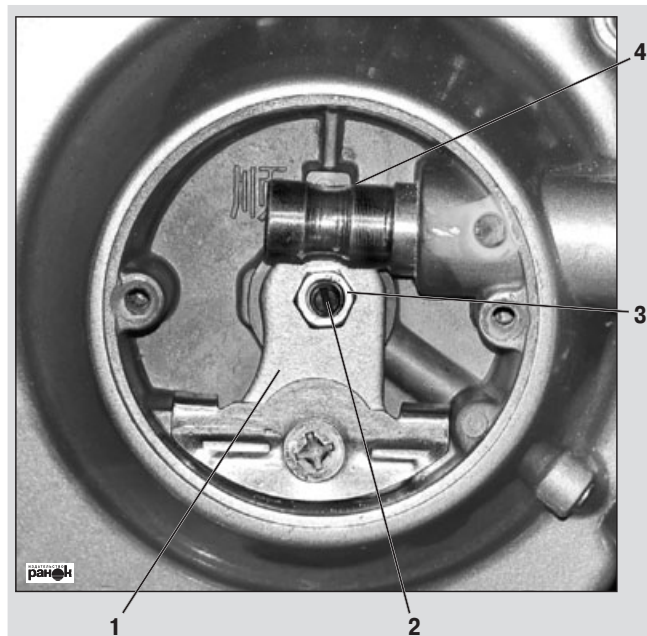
Расположение элементов привода и регулировки механизма выключения сцепления: 1 – рычаг привода механизма выключения сцепления; 2 – стопорная гайка («контргайка»); 3 – регулировочный винт механизма выключения сцепления; 4 – вал выжима сцепления
